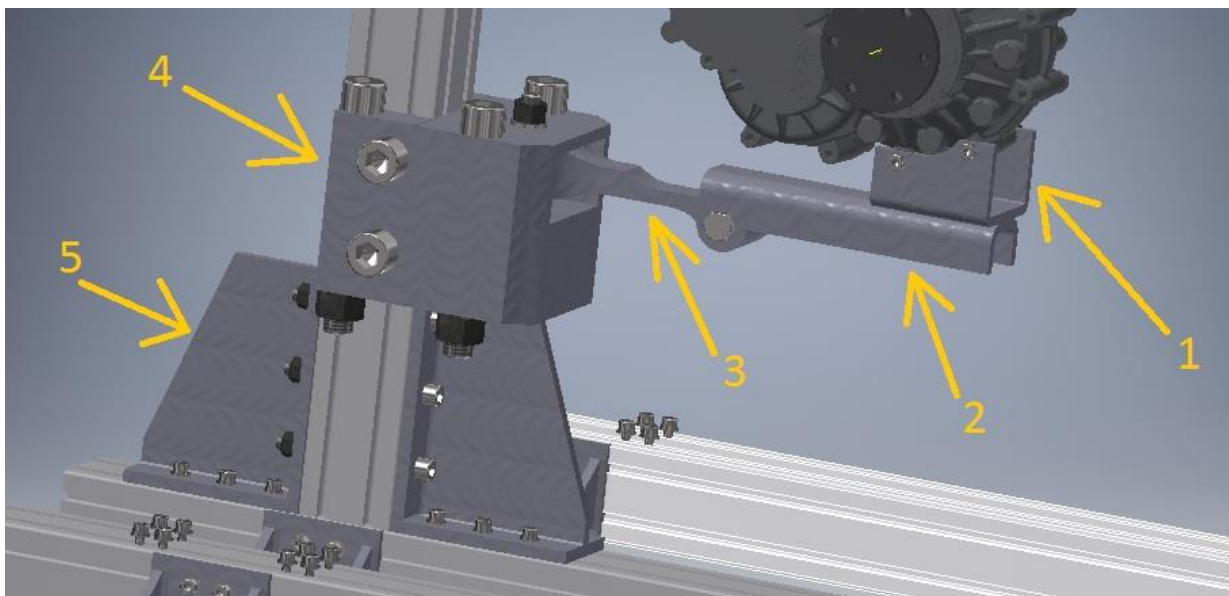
Uspořádání ramena pro uchycení soustavy elektromotor-převodovka.
